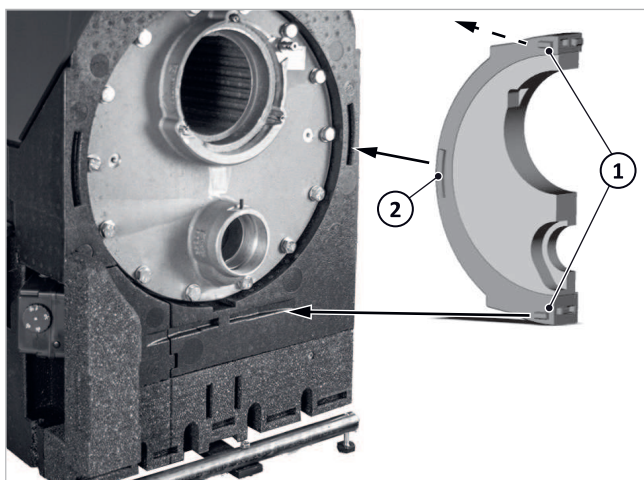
Aislamiento delantero de la brida (derecho, vista trasera) con muelles de bloqueo
